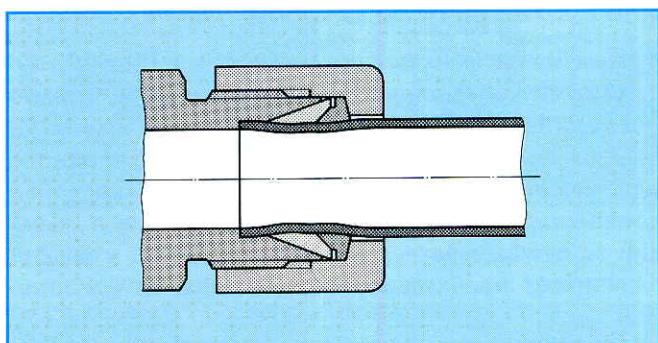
Резьбовое соединение с зажимным кольцом. Уплотнение: металл по металлу. Фиксация обеспечивается зажимом поверхности трубы.
